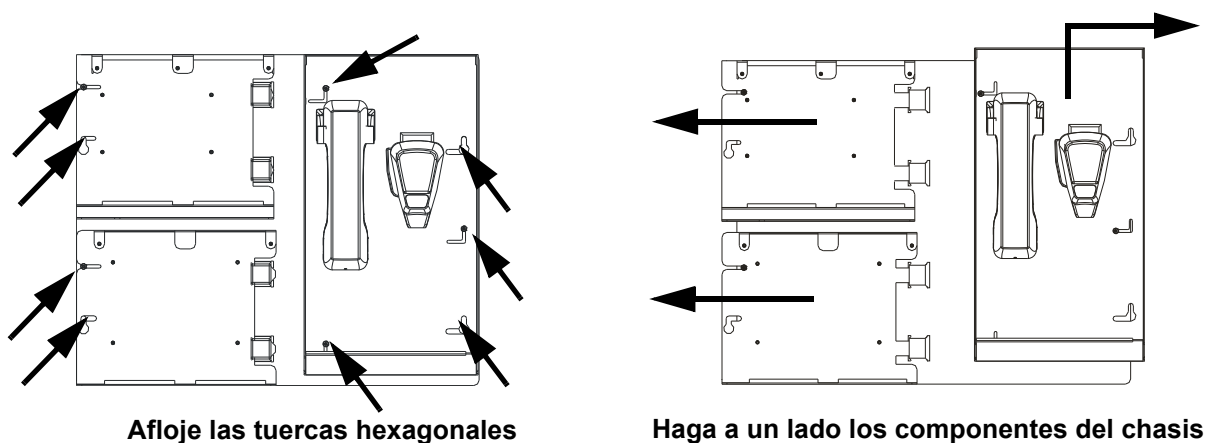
Hacer a un lado los componentes del chasis CA-2 para acceder al cableado
